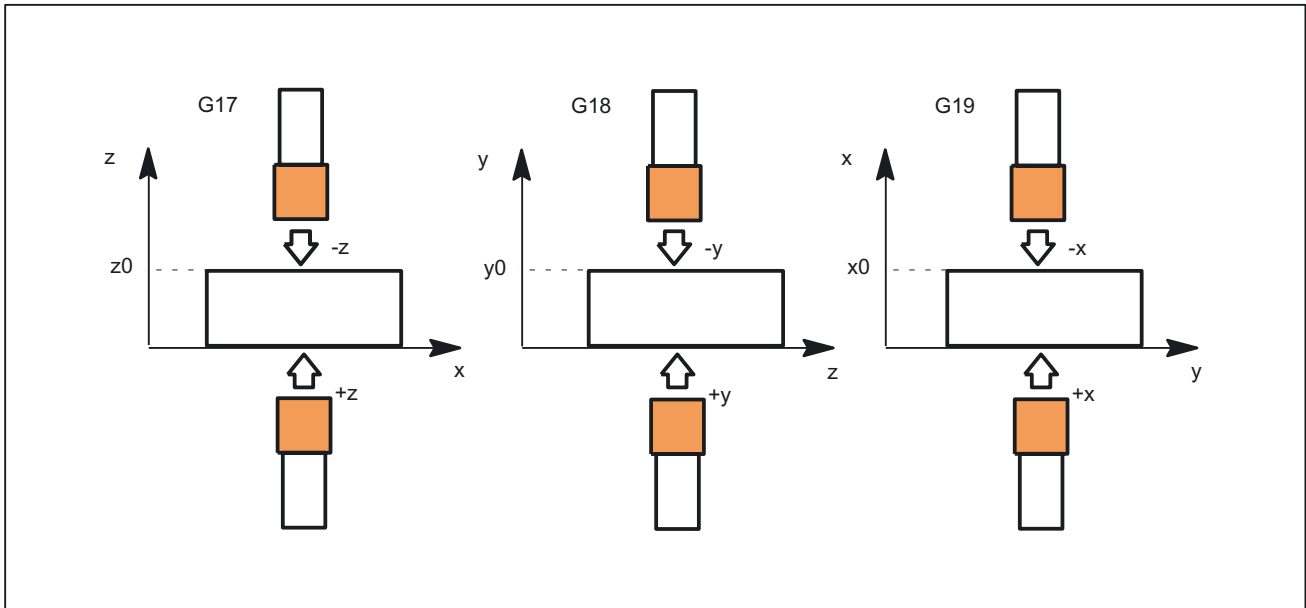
Werkzeuglängenvermessung für die ausgewählte Ebene G17, G18 und G19
